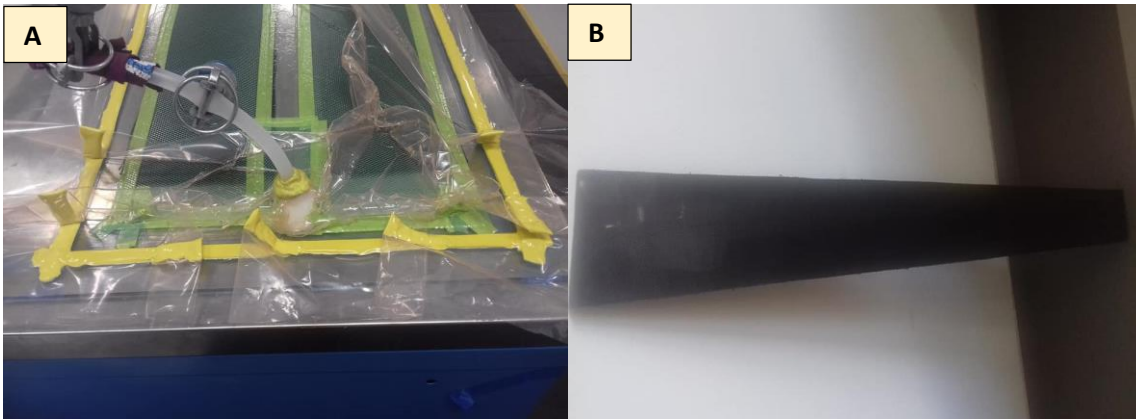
A) Construcción de los laminados, B) Viga sándwich manufactura en los laboratorios de CENTA.
